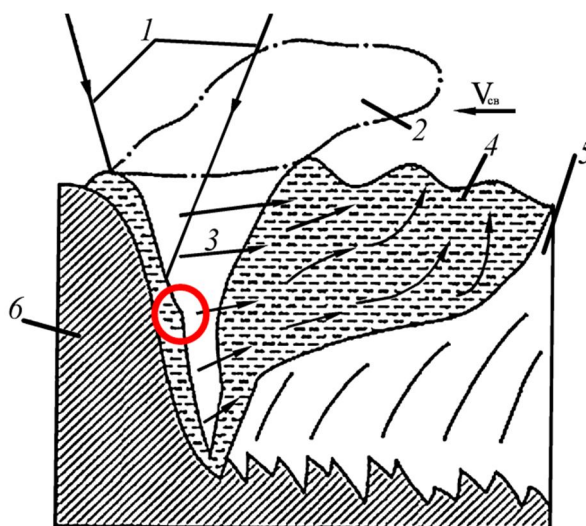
Схема сварочной ванны при лазерной сварке [13]:
